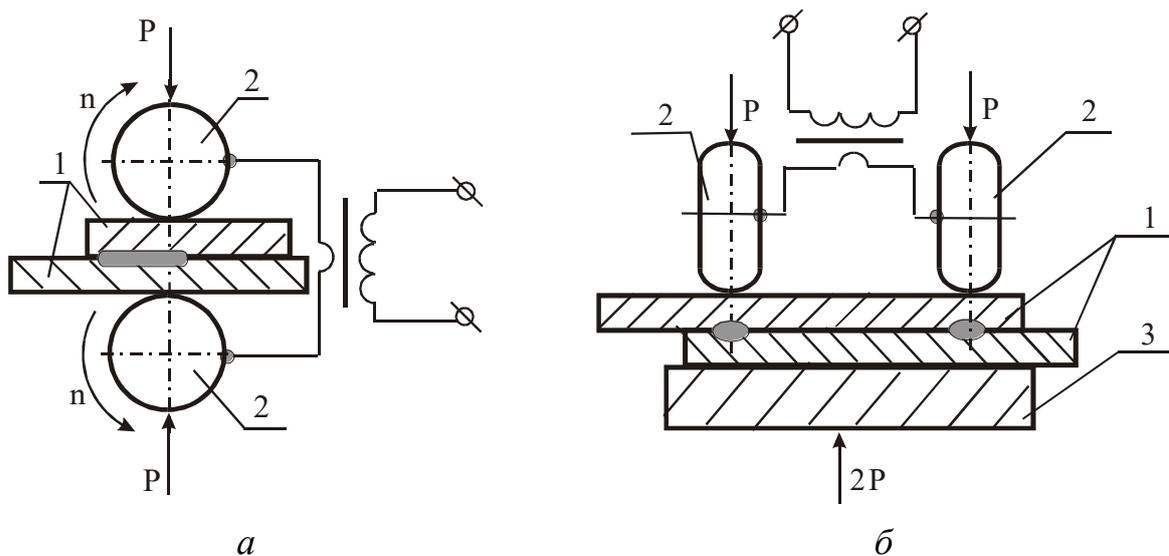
Схема двостороннього (а) і одностороннього (б) шовного зварювання: 1 – заготовки, 2 – електроди, 3 – мідна підкладка
